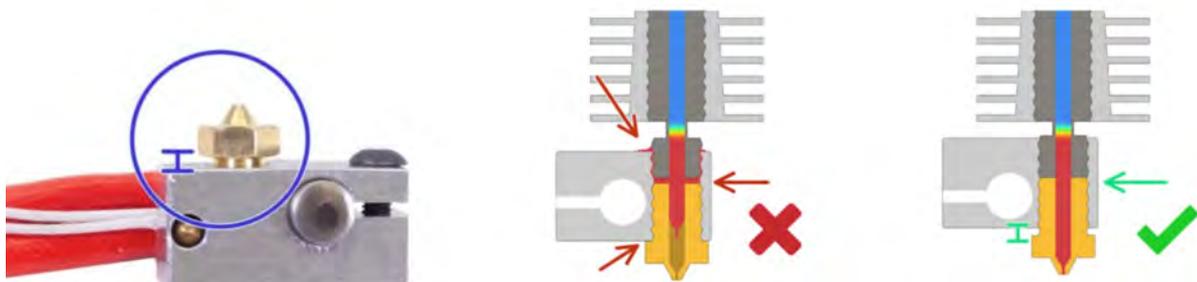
Ein Spalt zwischen einer vollständig eingeschraubten Düse und dem Heizblock
